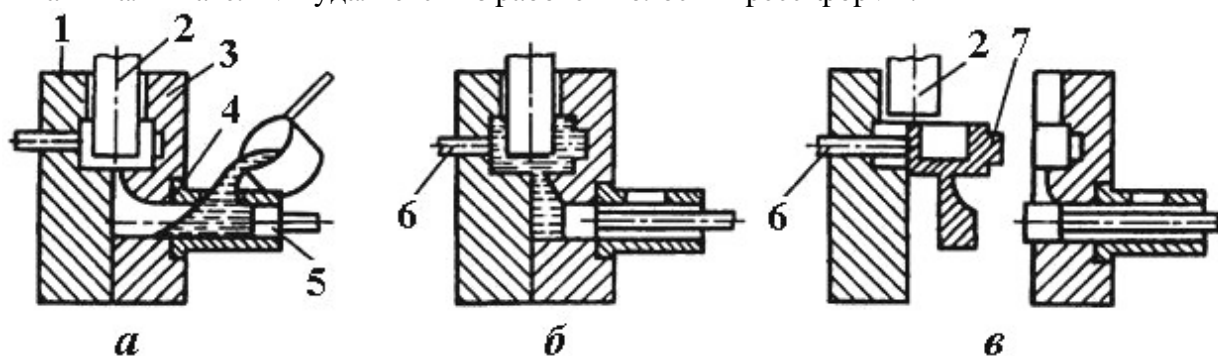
Схема процесса изготовления отливок на машинах литья под давлением с горизонтальной холодной камерой прессования: 1 – подвижная полуформа; 2 – стержень; 3 – неподвижная полуформа; 4 – камера прессования; 5 – плунжер; 6 – выталкиватели; 7 – отливка
